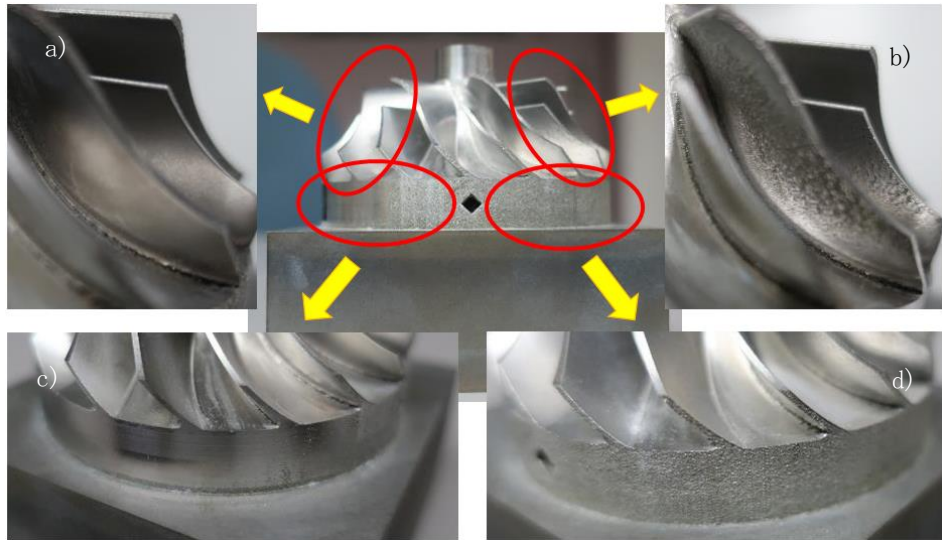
切削加工用試験片 B (オフセット量を変化させた) をベストフィット位置決め有で加工 (加工 3) した結果
